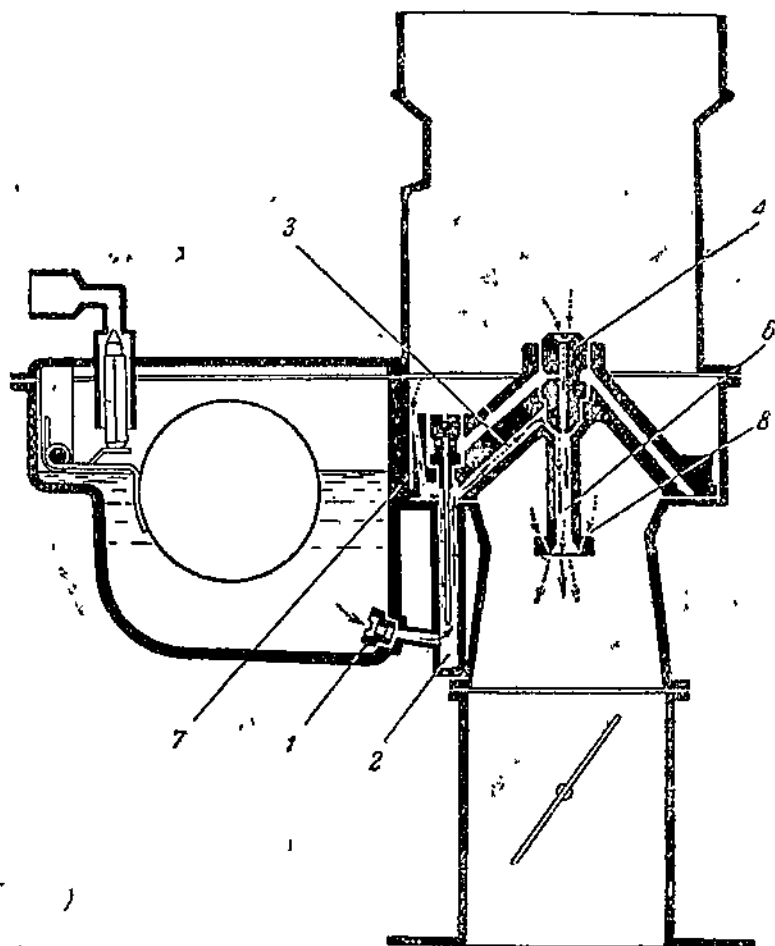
Схема работы компенсационного приспособления карбюратора Форд
